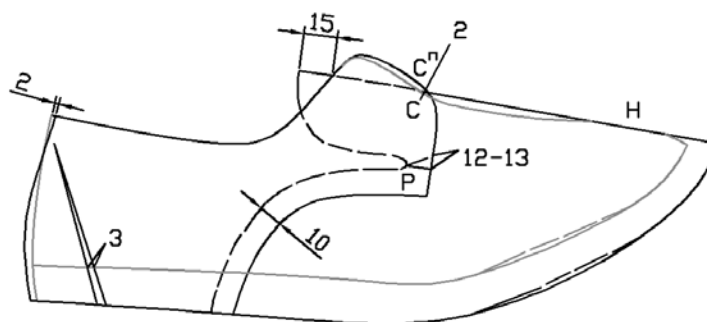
Конструктивная основа полуботинок с настрочными берцами «Дерби»
